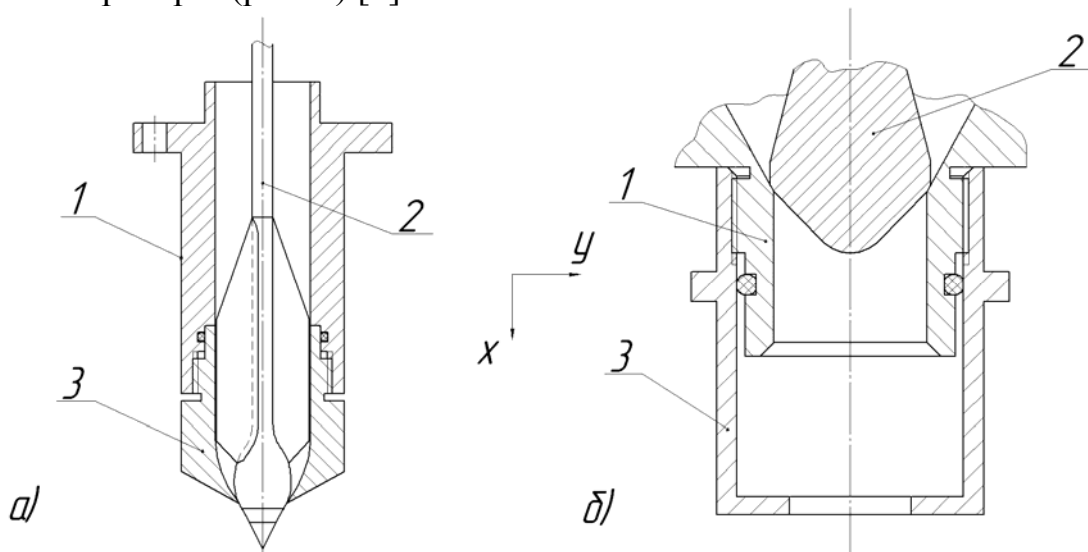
Приклад робочого органа у вагових дозаторах: а) конічна; б) циліндрична насадка: 1 – корпус; 2 – клапан; 3 – насадка
